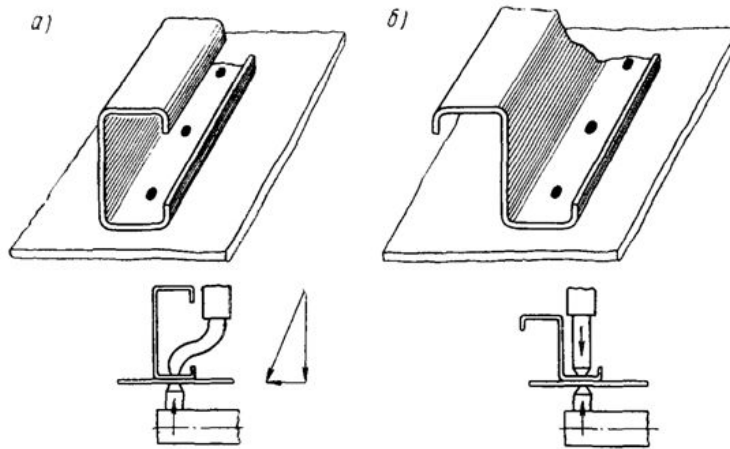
Примеры соединений при контактной точечной сварке:
